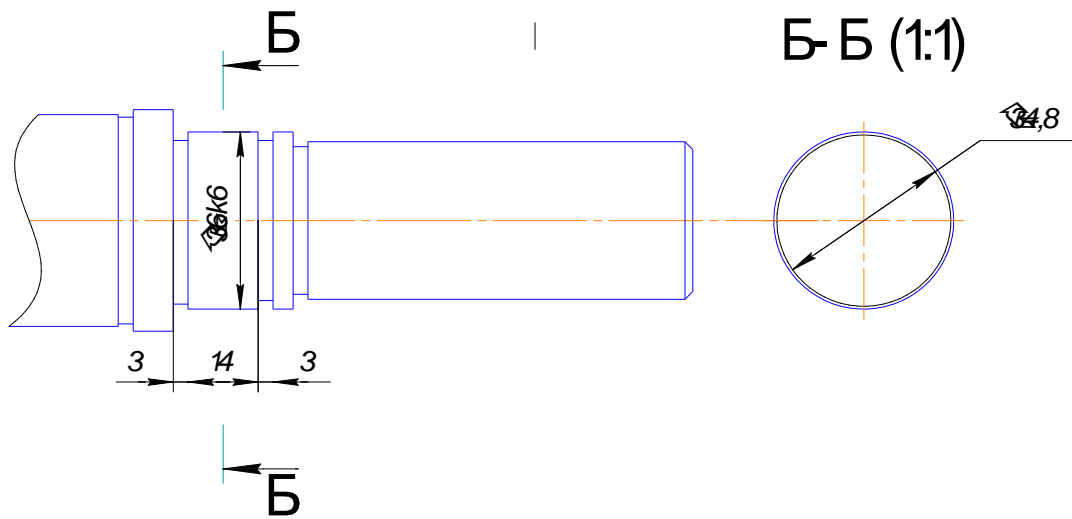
Поверхность 7 износ шейки вала – посадка под подшипники
